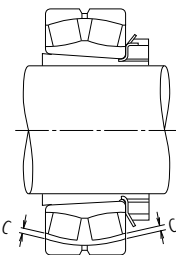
Medición del Juego de los Rodamientos de Rodillos Esféricos
